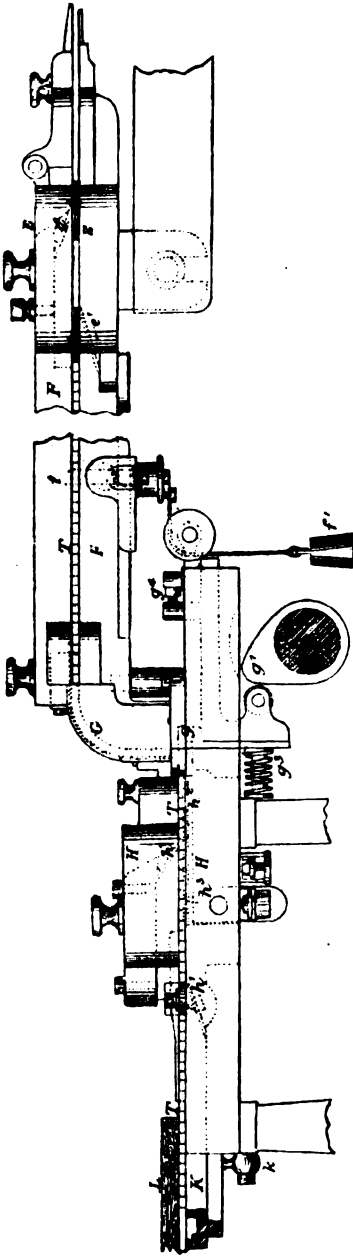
Fig. N. Zurichtapparat an Hepburns Komplettmachine.
